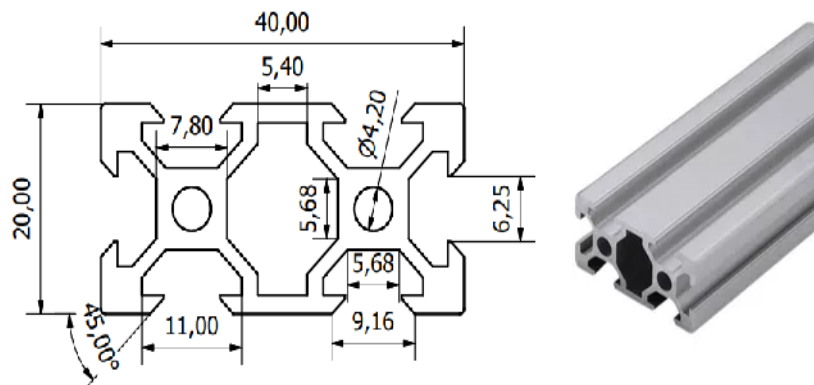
Perfil Alumínio Estrutural 40x20mm
